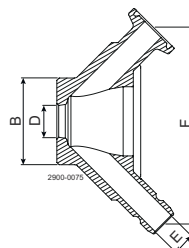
Ventilgehäuse: Tankschweißen
